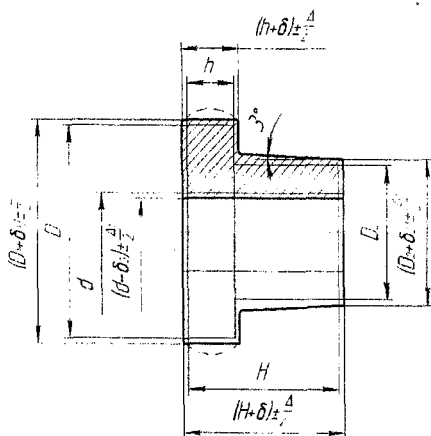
Схема назначения припусков и допусков для поковок 6-ой группы
